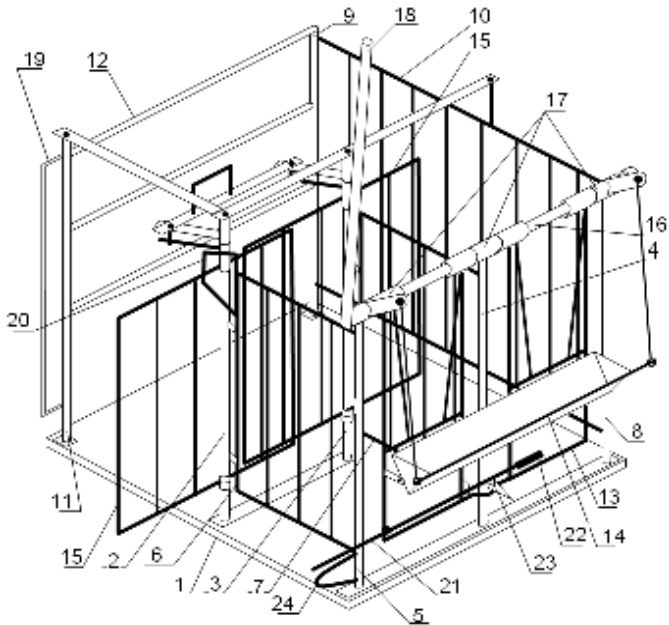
Конструкційно-технологічна схема двохстанкової установки лінійного типу для доїння овець
